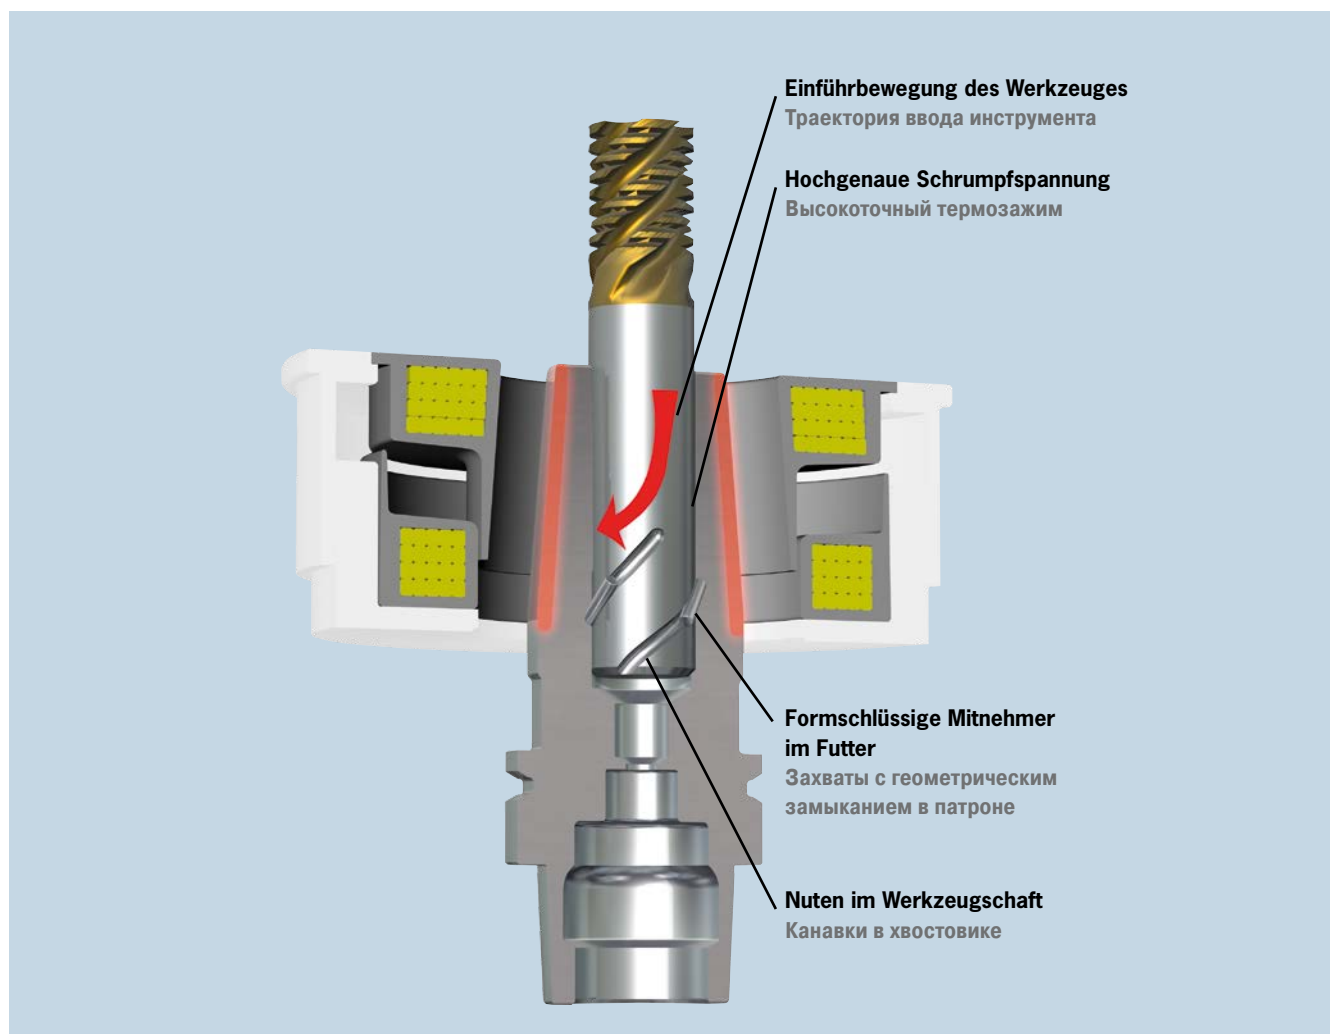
Mit Safe-Lock™ kein Werkzeugauszug
